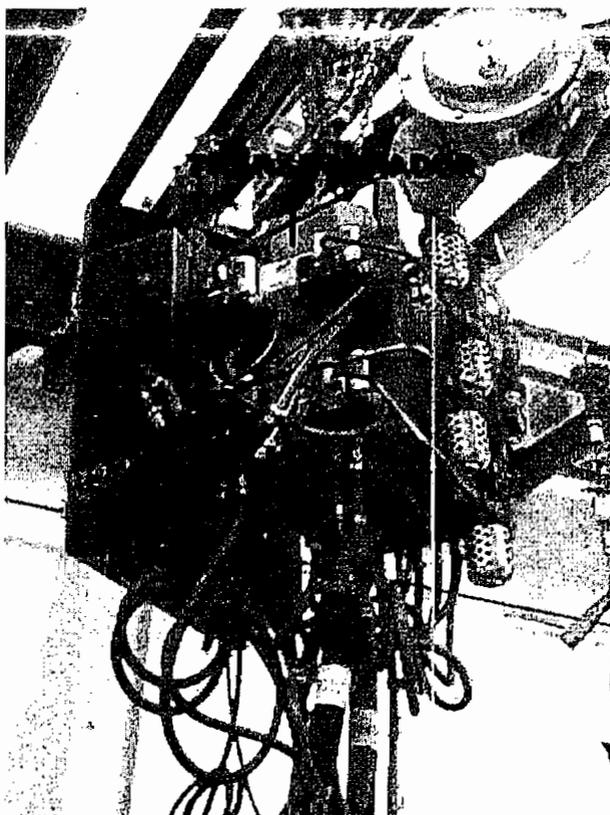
MÁQUINA DE TRANSFORMADOR COLGANTE. Transformador de soldadura.
